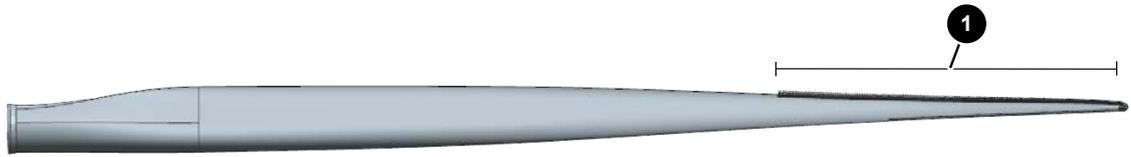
Position der Hinterkantenkammsegmente am Rotorblatt
